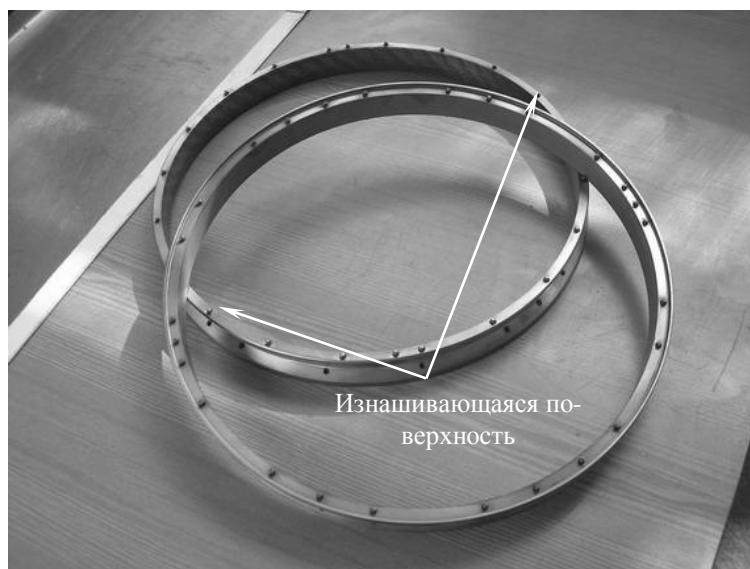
Кольца рабочих колес компрессора вертолетного двигателя (внешний вид)
